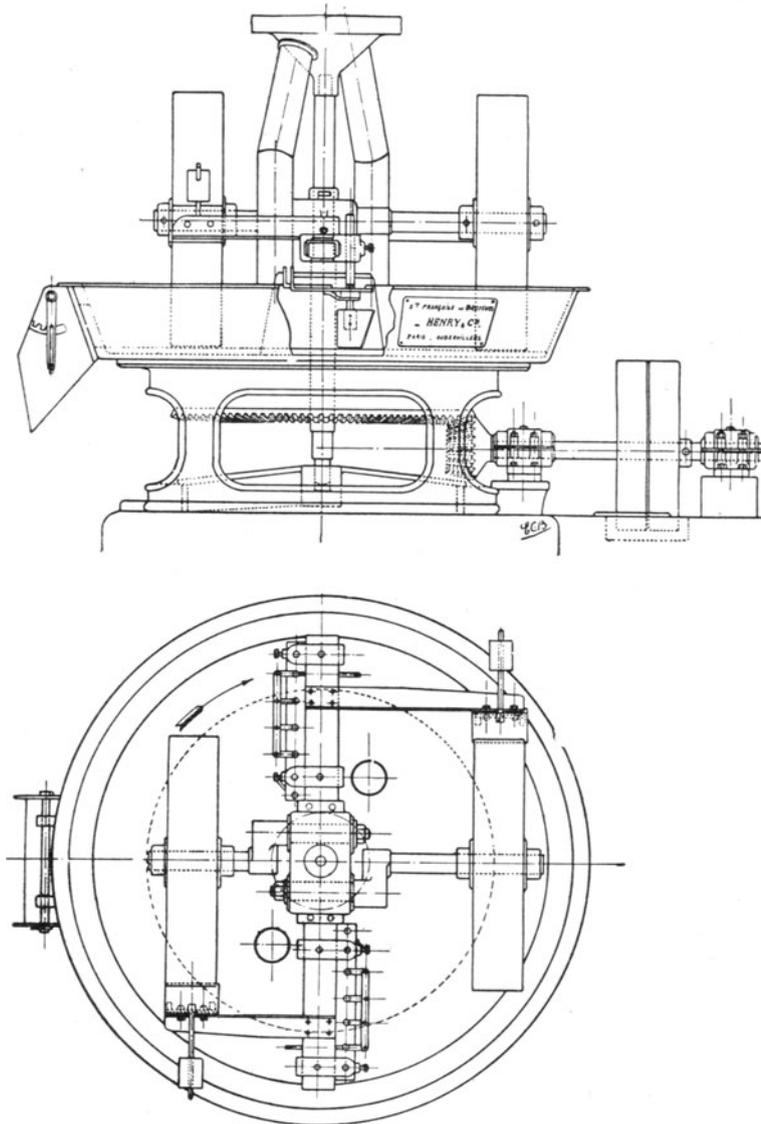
Kollergang mit feststehender Mahlbahn auf Gußständer.
